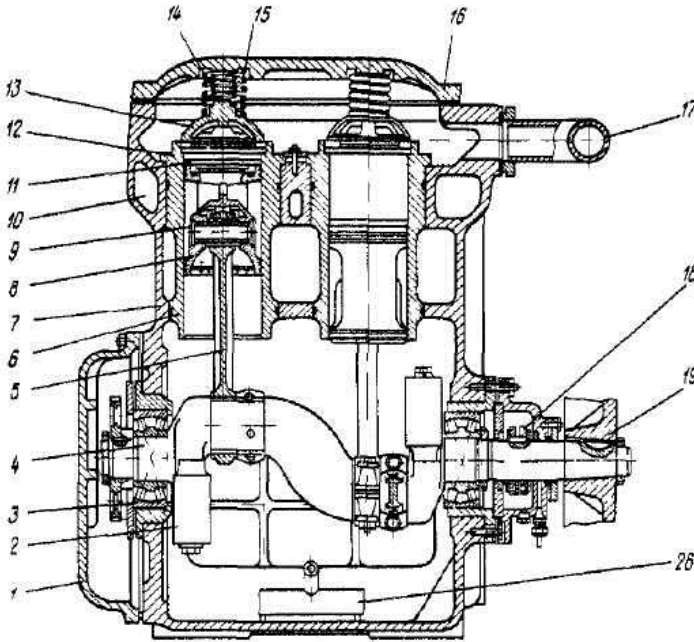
Не прямооточний компресор: 1 – кришка; 2 – противаги; 3 – корінний підшипник кочення; 4 – колінчастий вал; 5 – шатун; 6 – циліндрова гільза; 7 – блок-картер; 8 – прохідний поршень; 9 – поршневий палець; 10 – водяна сорочка; 11 – всмоктувальний клапан; 12 – клапан нагнітальний; 13 – притискна склянка; 14 і 13 – буферні пружини; 16 – кришка блоку циліндрів; 17 – нагнітальний колектор; 18 – сальник; 19 – ступиця маховика; 20 – вентиль нагнітальний запірний; 21 – пропускний вентиль; 22 – фільтр всмоктувальний; 23 – порожнина всмоктування; 24 – бічні кришки; 25 – оглядове скло за рівнем мастила; 26 – фільтр масляний грубого очищення; 27 – всмоктувальний вентиль; 28 – манометр
